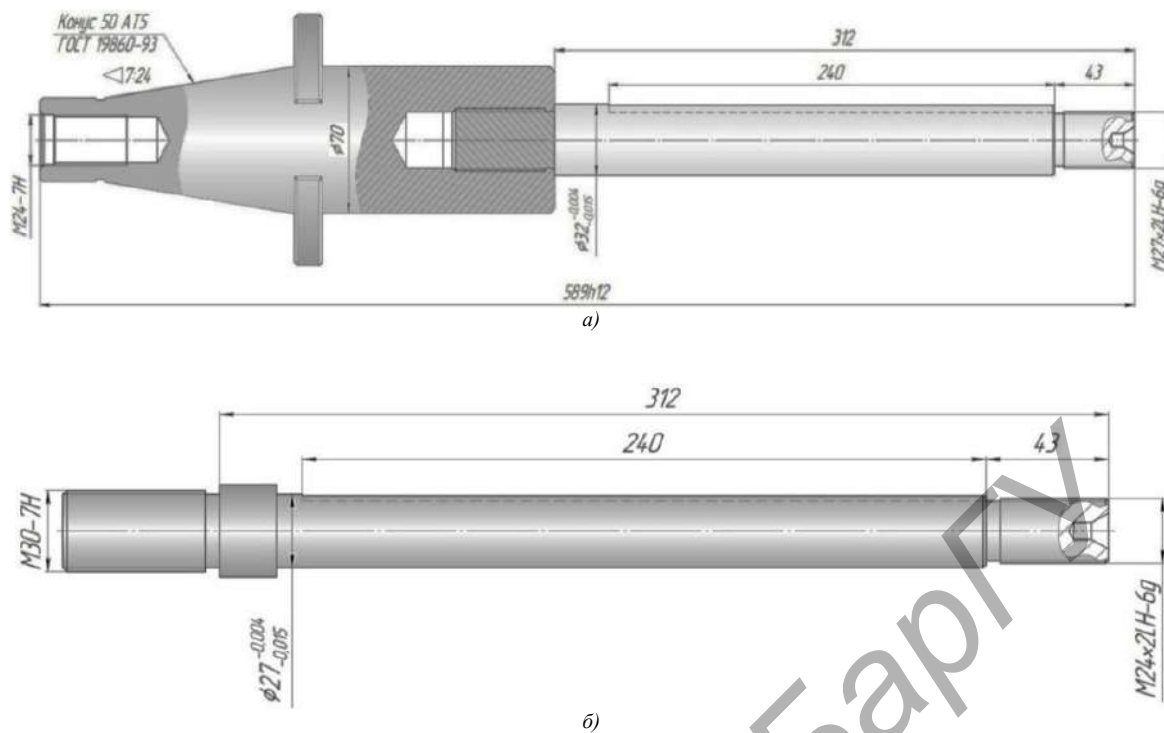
Конструкция модульной фрезерной оправки для насадных фрез
